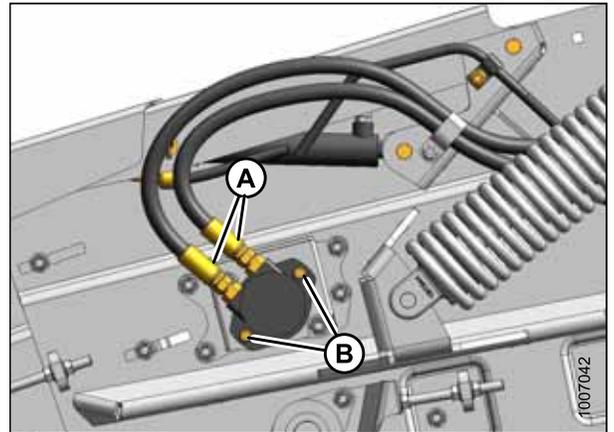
Motor hidráulico delantero; lado izquierdo
